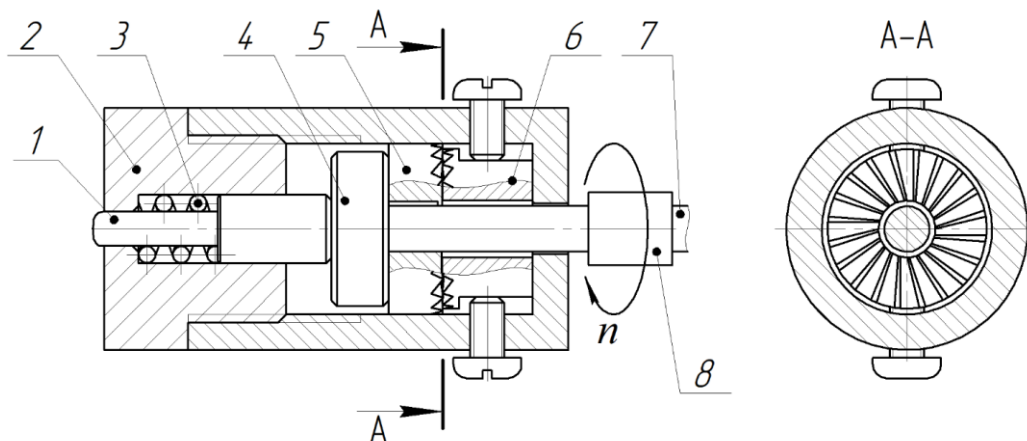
Общий вид устройства для поверхностно-пластического упрочнения
